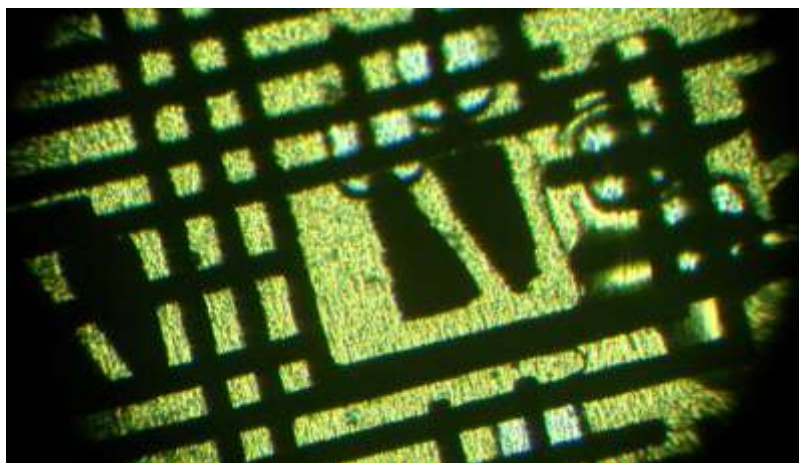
Сварочное соединение, окно сварки, зонд.
